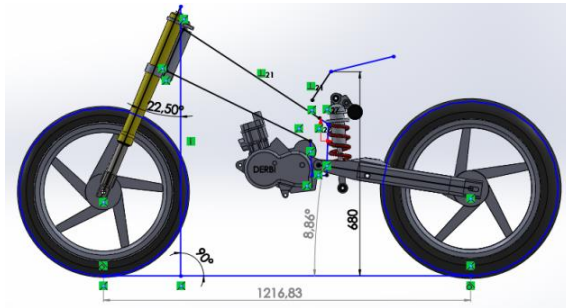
Posicionamiento de componentes sobre croquis de geometrías.
